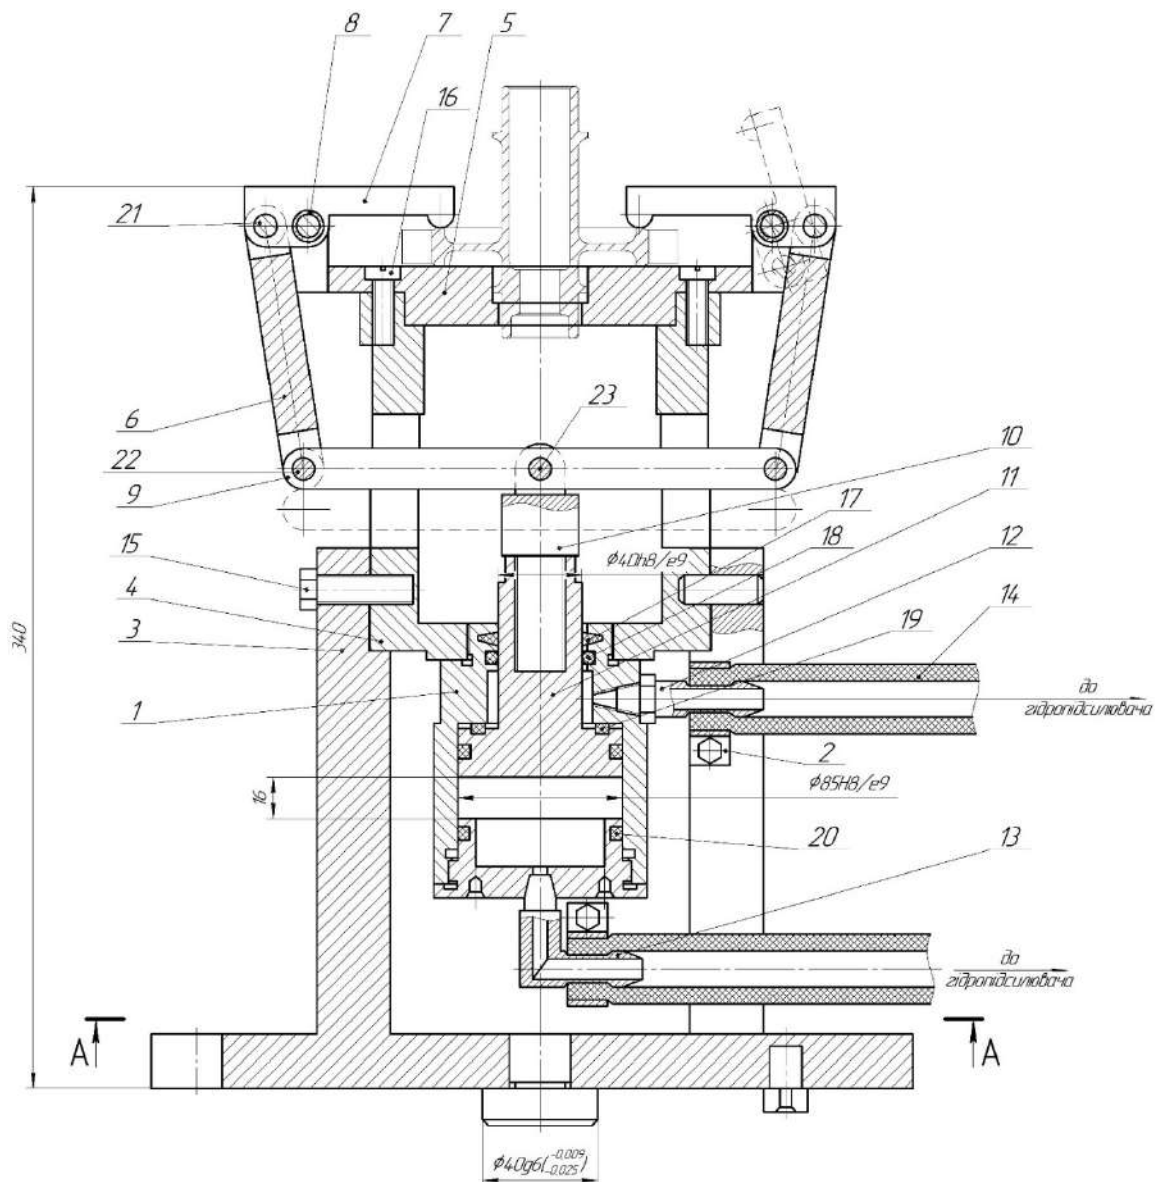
Пристосування для фрезерування лисок операція №090
